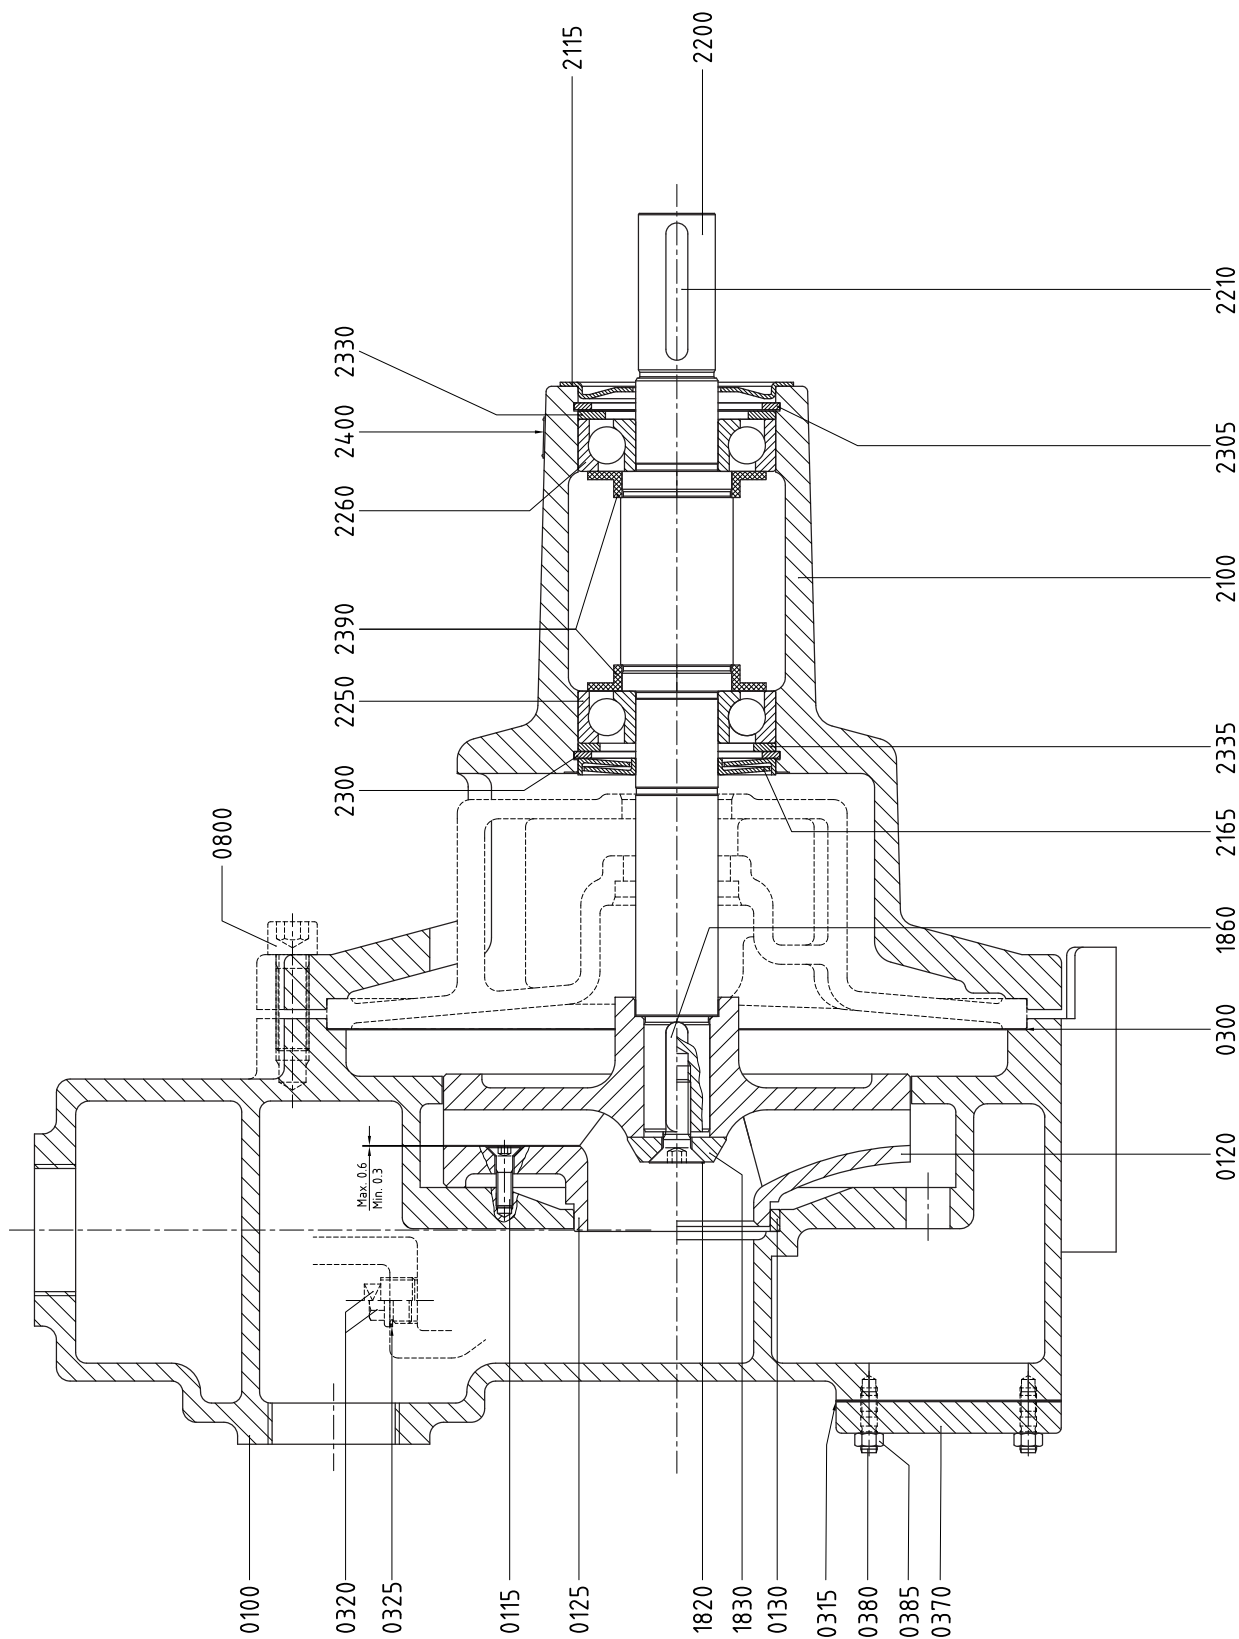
Desenho em corte FRE - grupo de rolamento 3.
